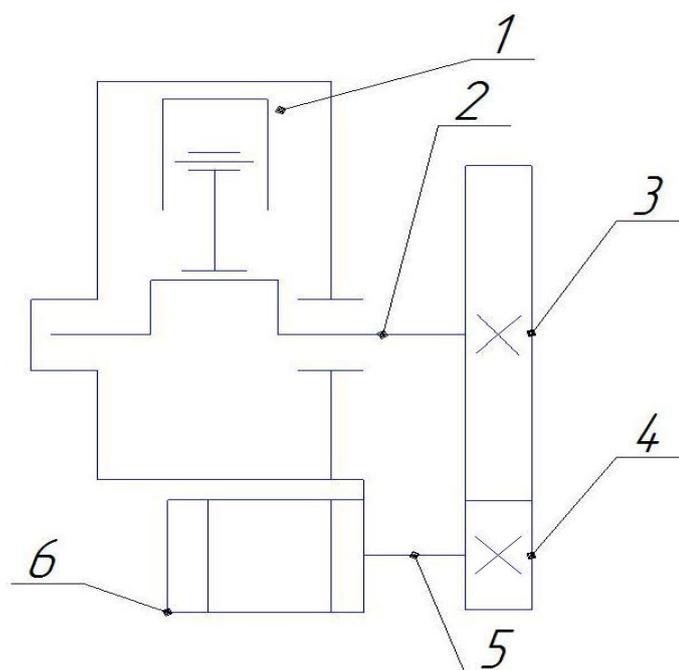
Кинематическая схема автономного стенда для холодной обкатки ДВС: 1 – кривошипно-шатунный механизм; 2- коленчатый вал; 3 - зубчатый венец маховика; 4 – ведущая шестерня; 5 – вал электродвигателя; 6 -высокочастотный электродвигатель.
